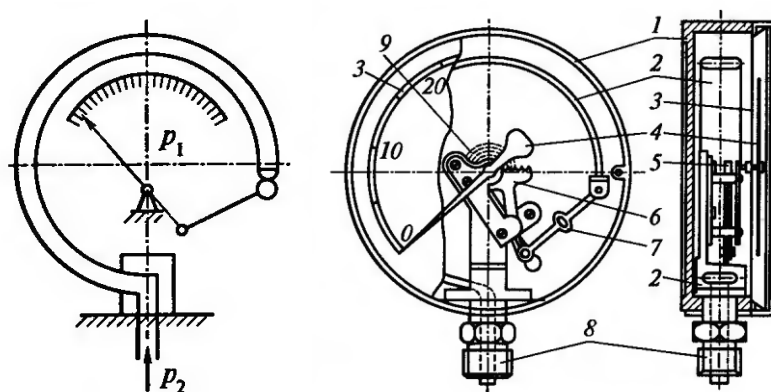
Устройство пружинного манометра: 1 – корпус; 2 – полая трубка; 3 – шкала; 4 – стрелка; 5 – шестерня; 6 – зубчатый сектор; 7 – поводок; 8 – штуцер; 9 – пружина.
